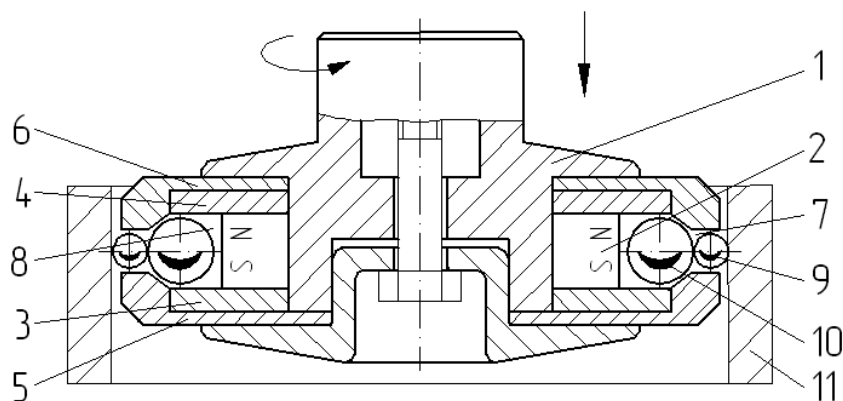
Двухрядный магнитно-динамический раскатник
